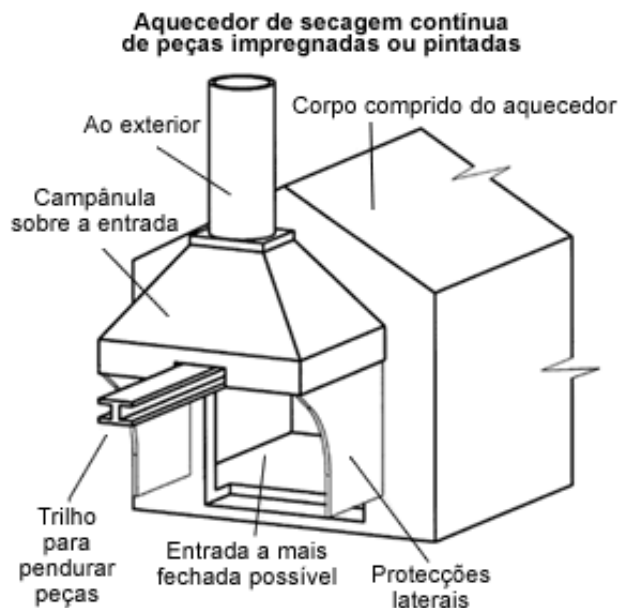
Aquecedor de secagem contínua de peças impregnadas ou pintadas
